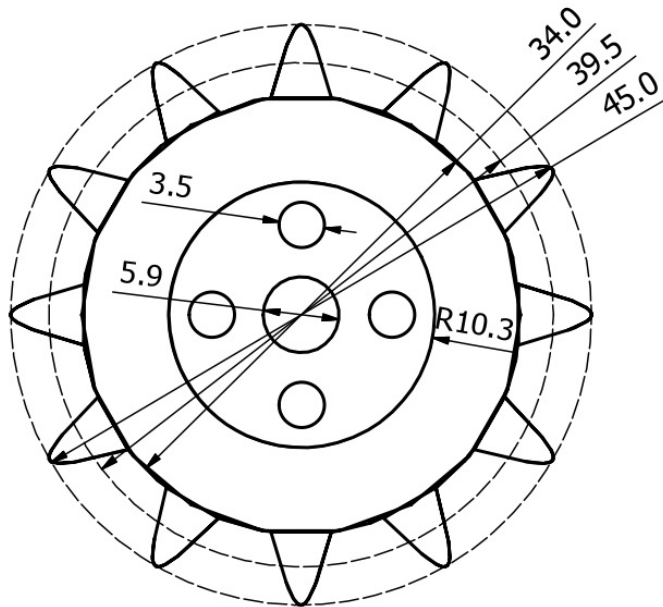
Dimensiones engrane acoplado al servomotor. Medidas en [mm].
